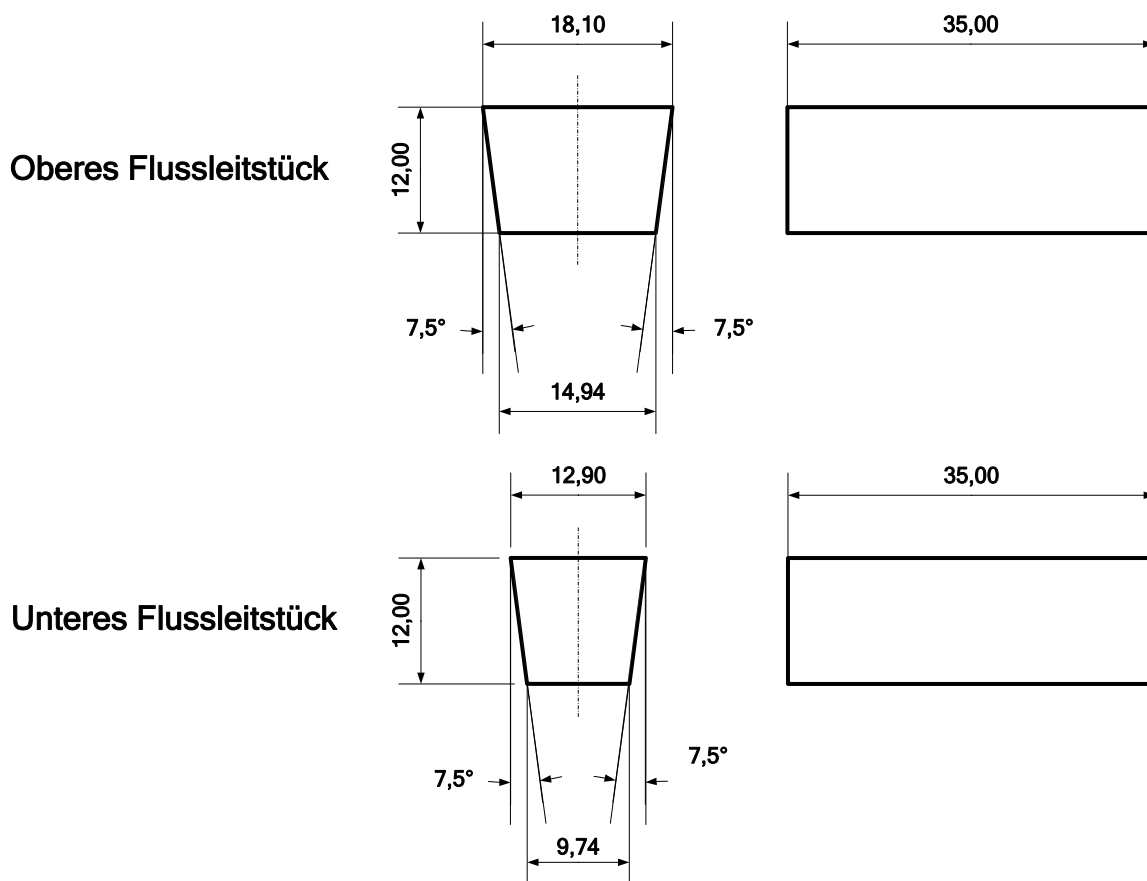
Technische Zeichnung der gefertigten Flussleitstücke für den Rotor
